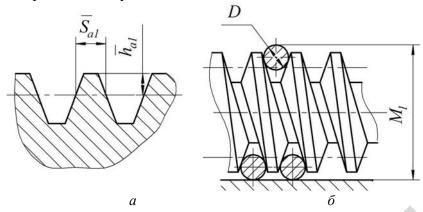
Показатели для контроля взаимного положения разноименных профилей витка червяка
